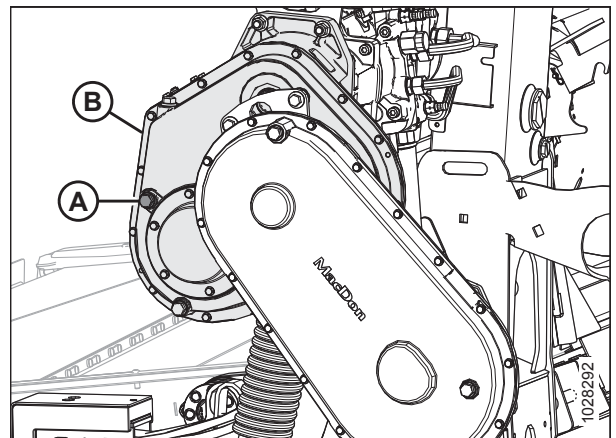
Caja de engranajes principal del mando de la plataforma
